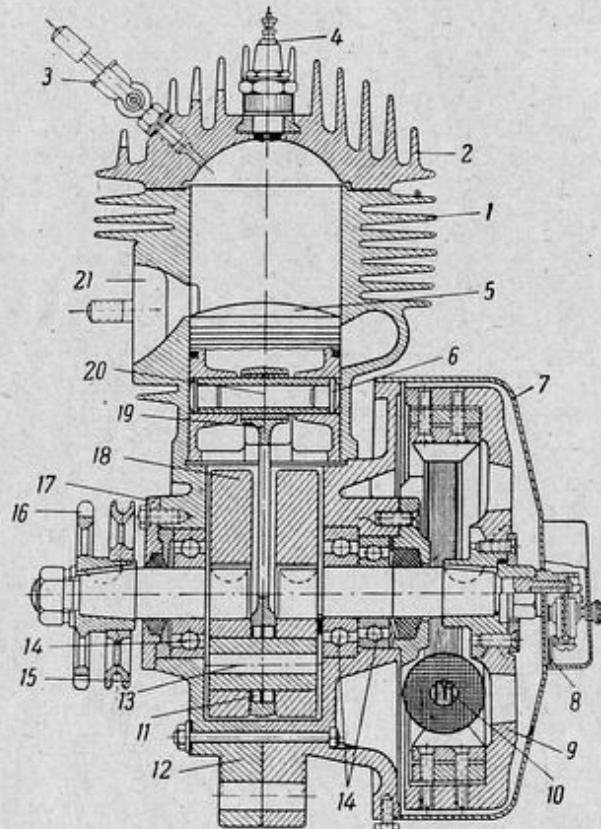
Двухтактный одноцилиндровый двигатель ИЖ-8 с рабочим объёмом 300 см^3 :
